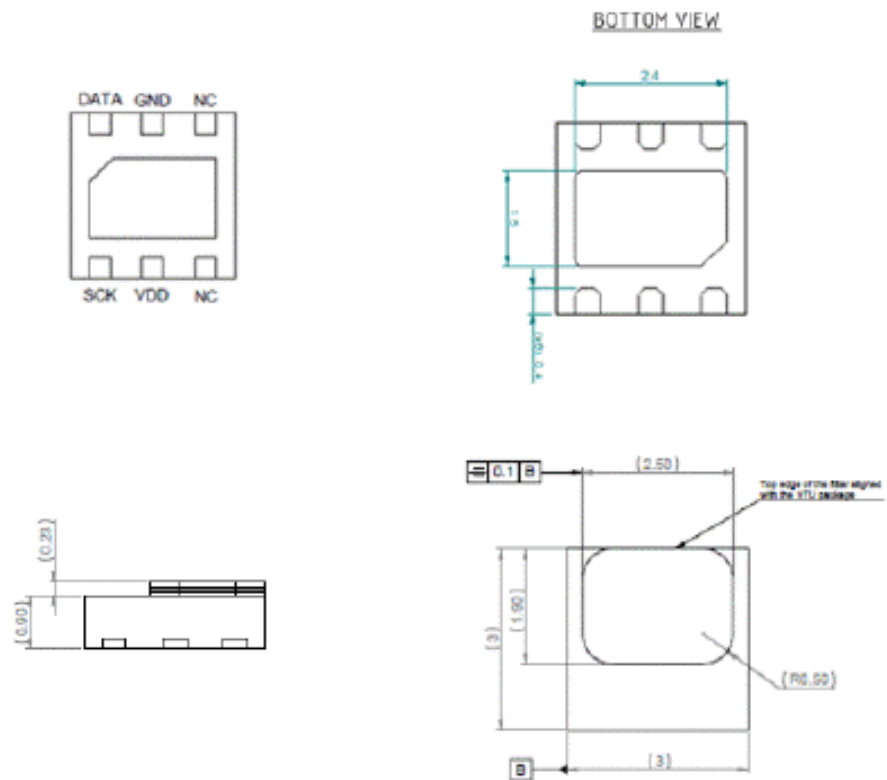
Dimensiones de montaje del sensor HTU20D(F) en mm [64].
